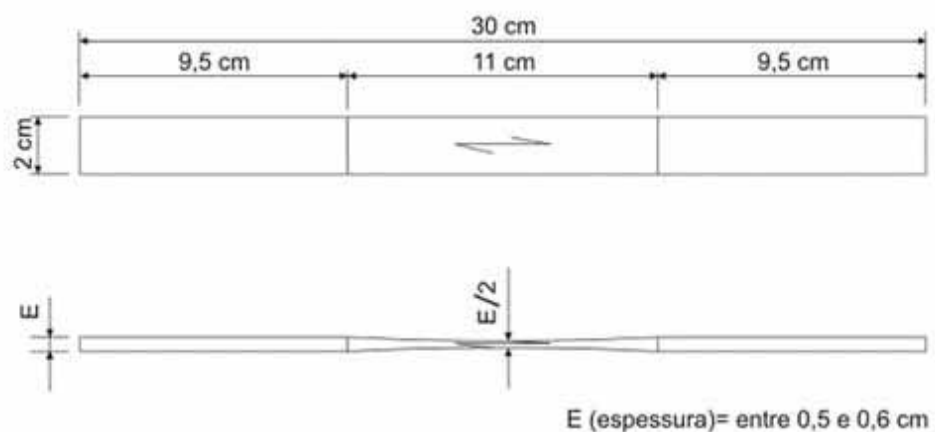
Dimensões do corpo de prova para o ensaio de tração.
